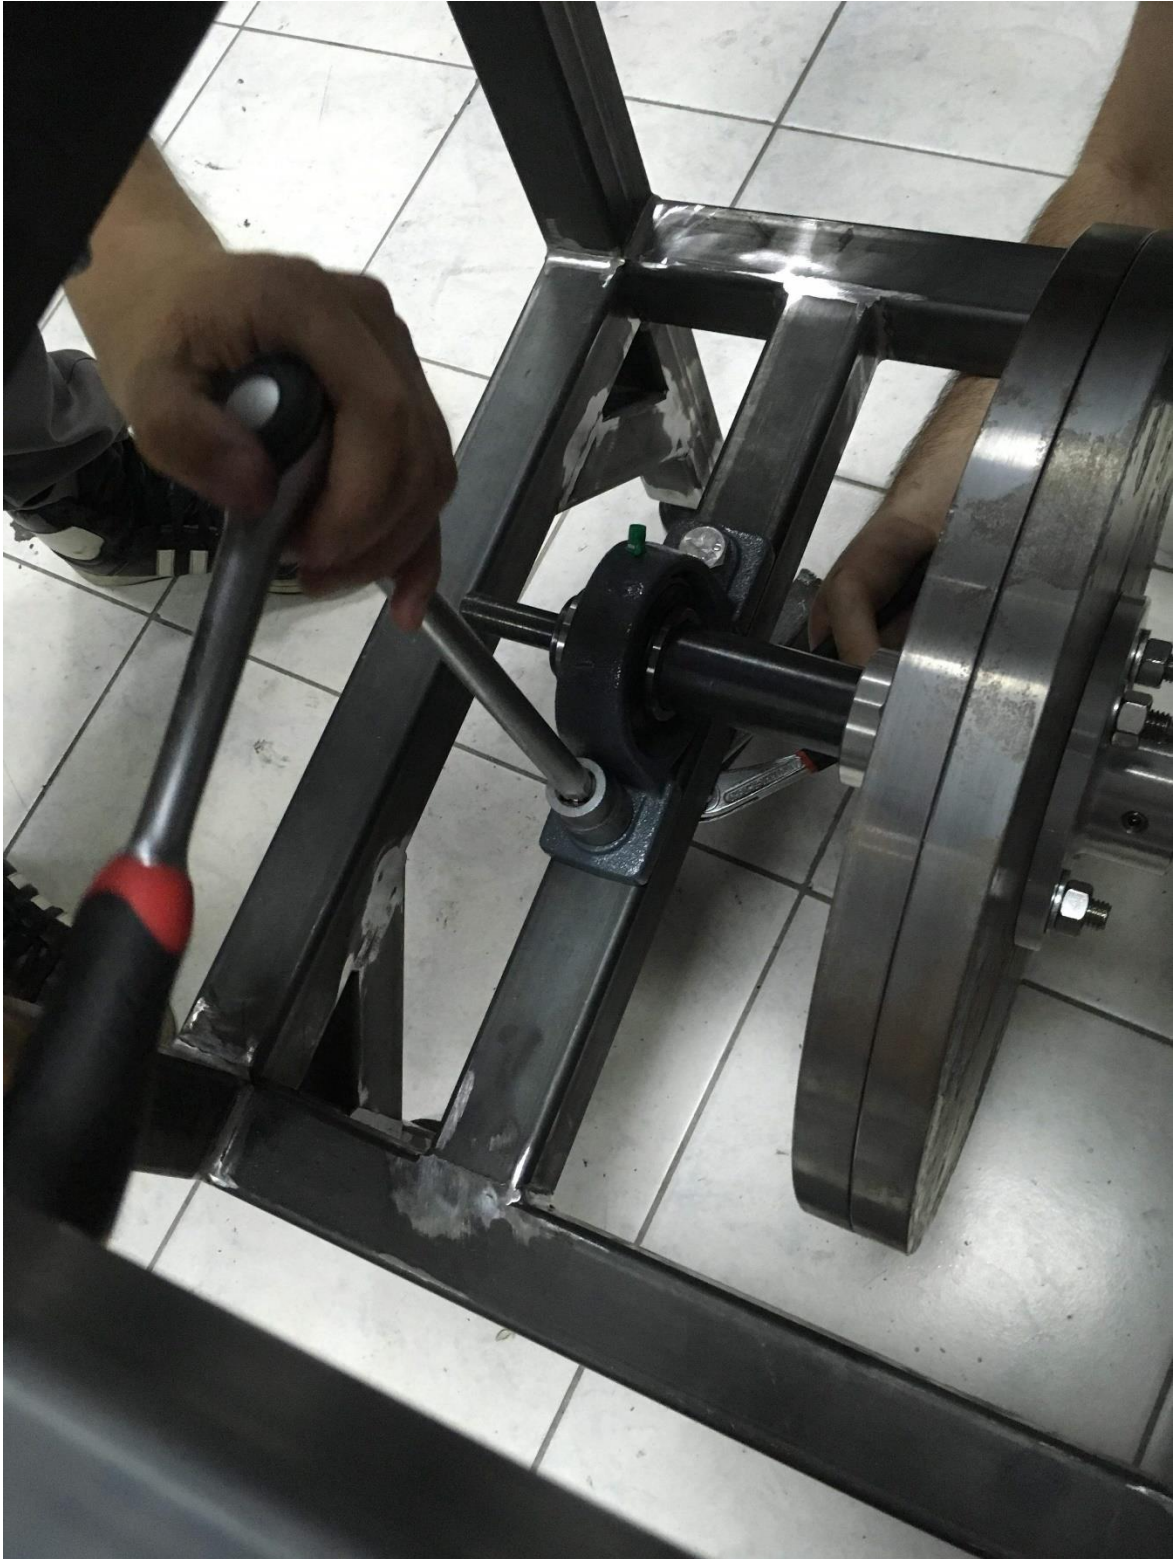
Τελικό Συναρμολόγημα. POS20_CD_FLYWHELL SUB ASSEMBLY.
